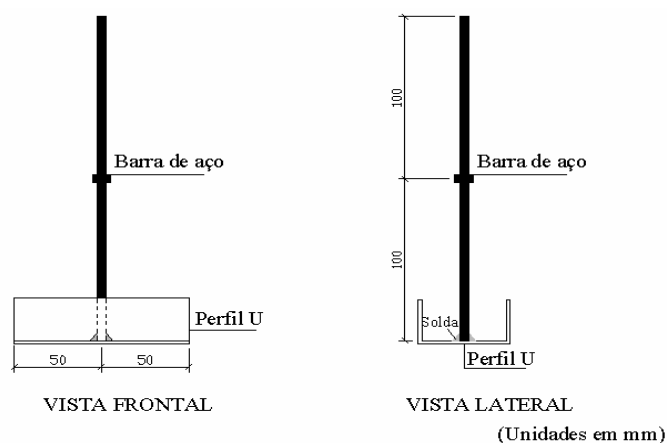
Corpo-de-prova para ensaio de ligação soldada
